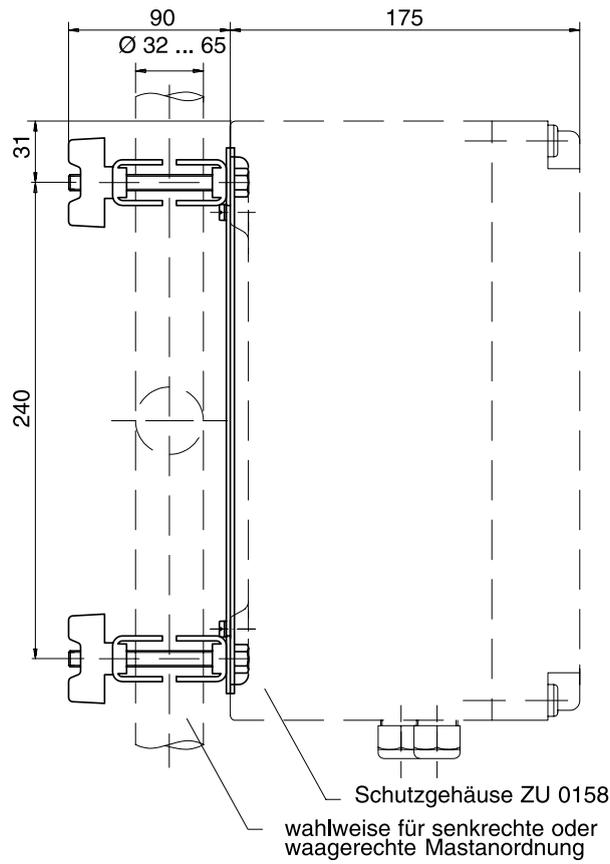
Mastschellen-Satz ZU 0220 für Schutzgehäuse ZU 0158
